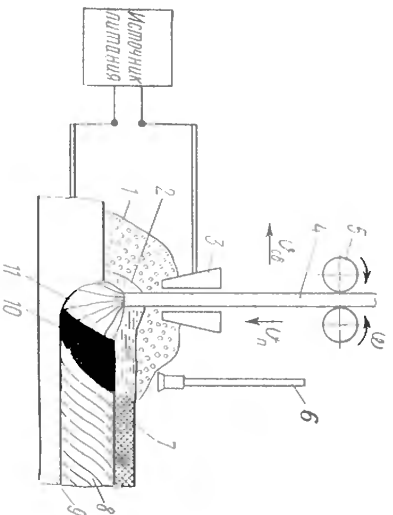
Схема дуговой сварки под флюсом:
